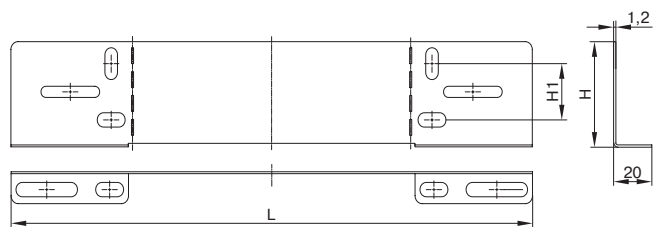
Редукция для лотков лестничных H80–H150 / Figure D.2 — Cable ladder reducer H80–H150
